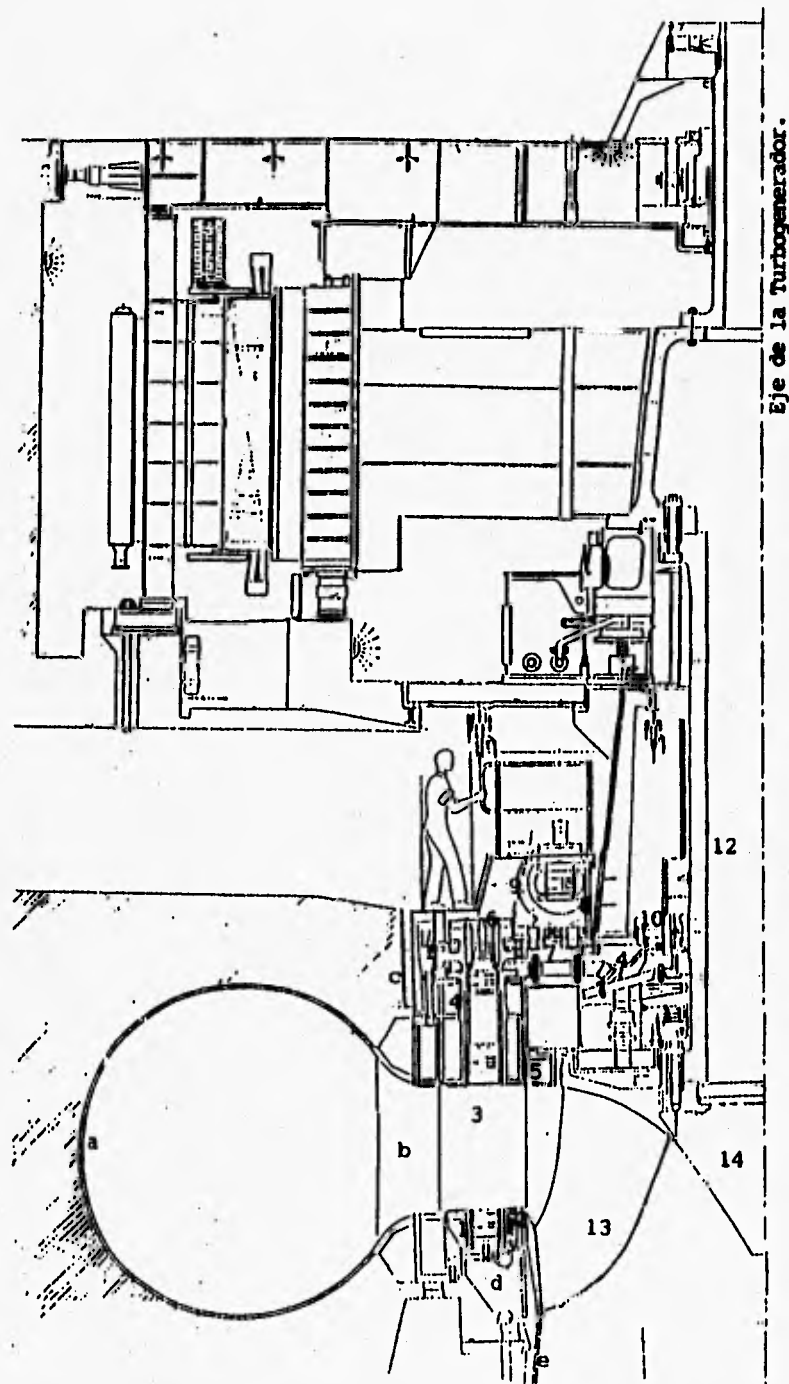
CORTE LONGITUDINAL DEL CONJUNTO TURBINA (MECANISMOS) Y GENERADOR.
